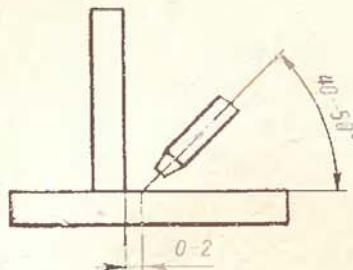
Схема полуавтоматической сварки в углекислом газе тавровых соединений
